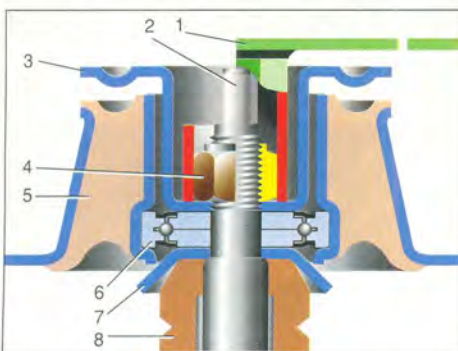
Так отворачивают гайку штока амортизатора: 1 – ключ для гайки; 2 – шток; 3 – ограничитель хода верхней опоры; 4 – гайка; 5 – верхняя опора; 6 – подшипник; 7 – верхняя опорная чашка; 8 – буфер хода сжатия.
